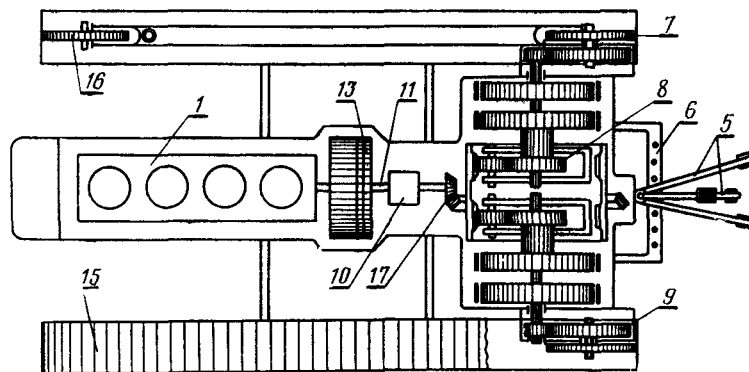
Схема расположения основных механизмов и сборочных единиц гусеничного трактора ДТ-75:
